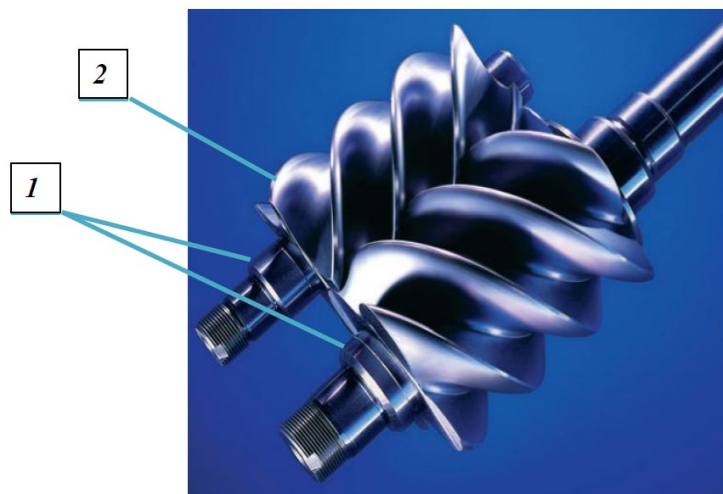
Місця зносу роторів гвинтового компресора: 1 - посадочні місця під підшипники; 2 - робочі поверхні стрічок
